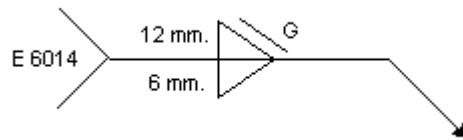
Ejemplo de símbolo de soldadura
